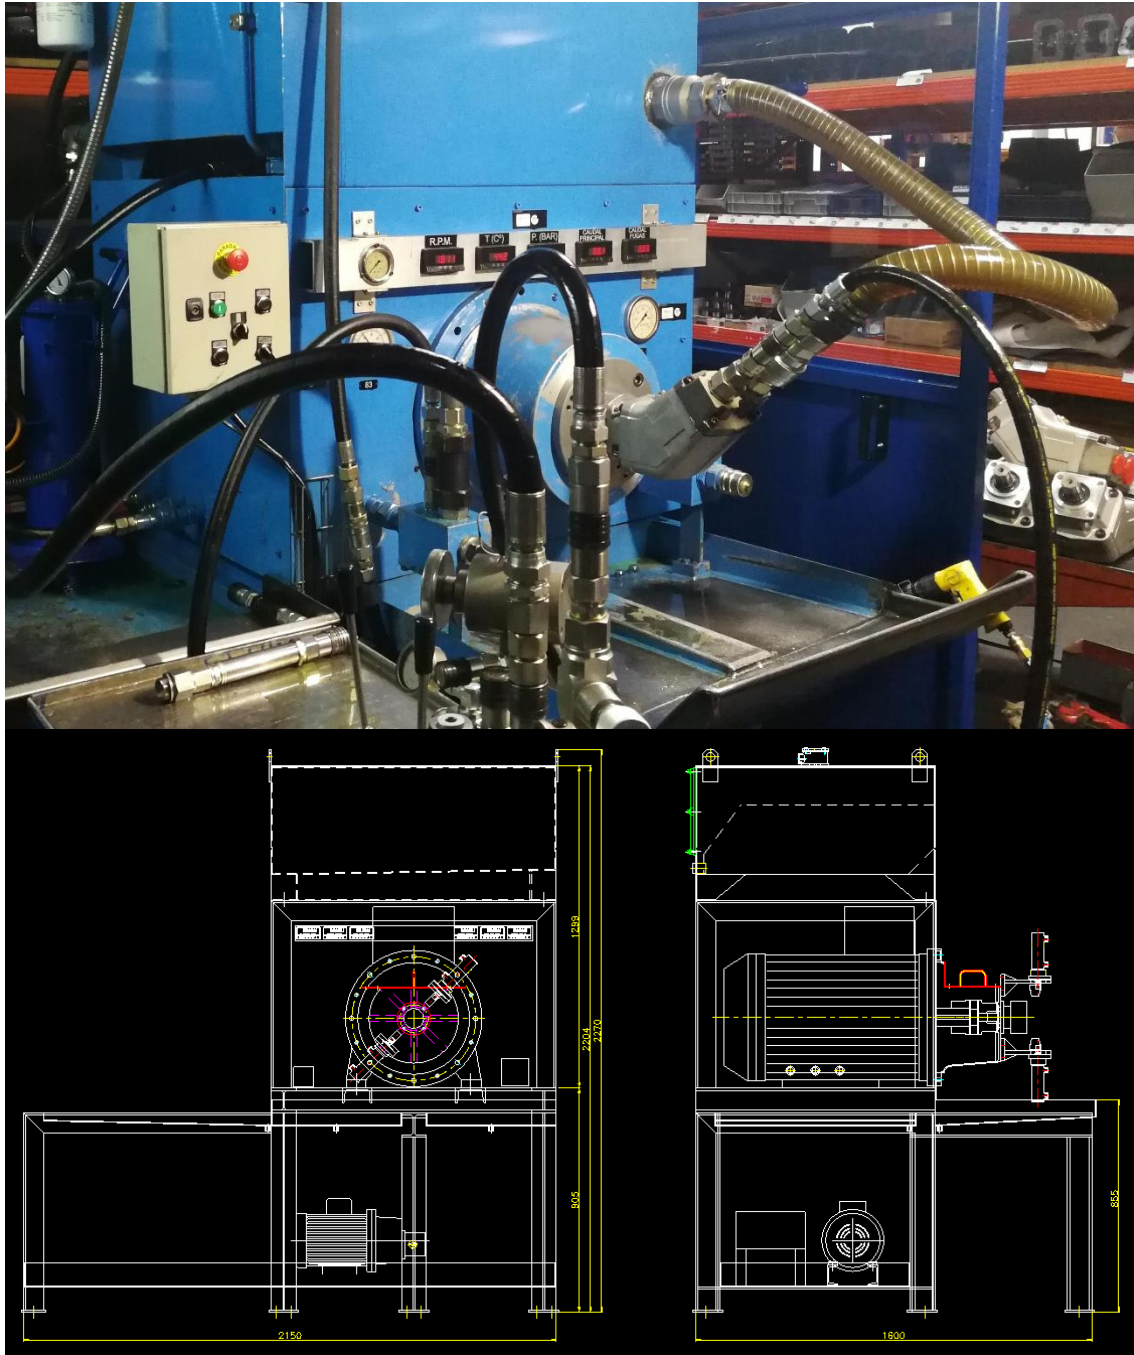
Fotografia/Esquema 3D - Máquina de testes
